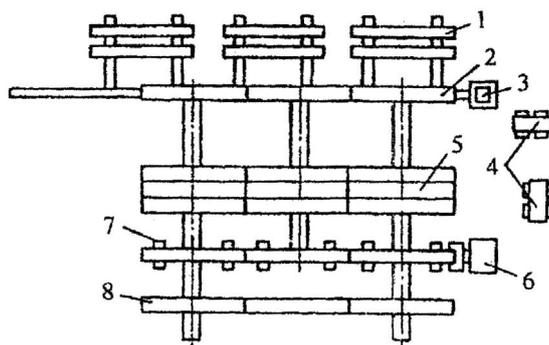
Схема полевой сварочной базы ПАУ-600 для сварки труб электродуговой сваркой под флюсом:
